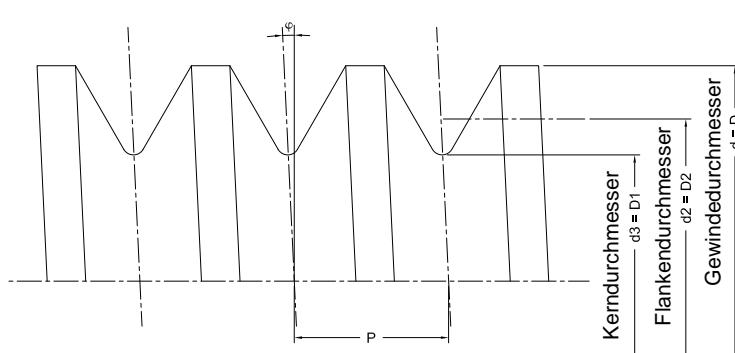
Linksgewinde bei Rechtslauf der Maschinenspindel
